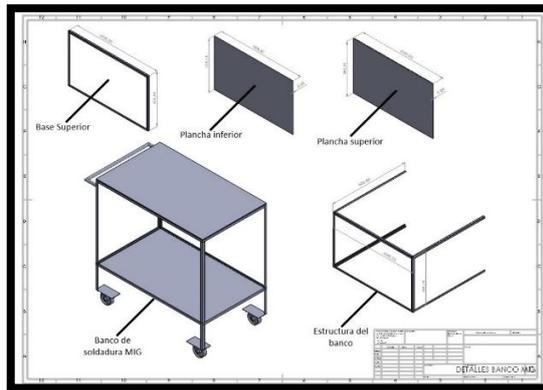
Especificaciones y medidas del banco de soldadura MIG.
